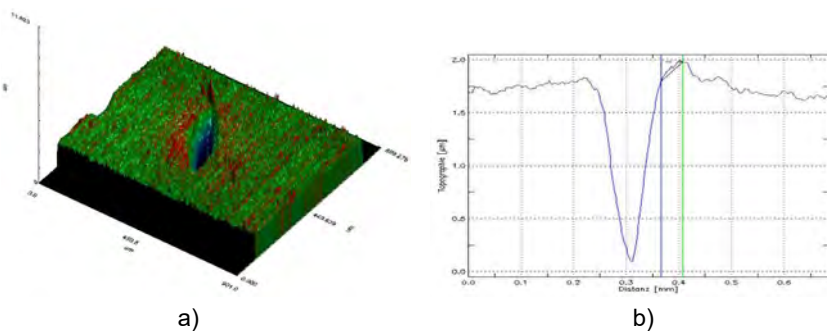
Lustruire 8 ore: a) lovitura 3D, b) profil lovitură
